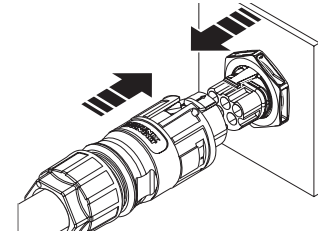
AC-Anschlussstecker mit dem Gerätestecker einrasten
